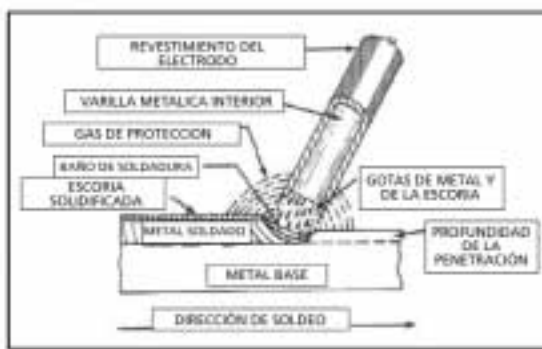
Proceso de soldadura manual por arco con electrodo revestido
